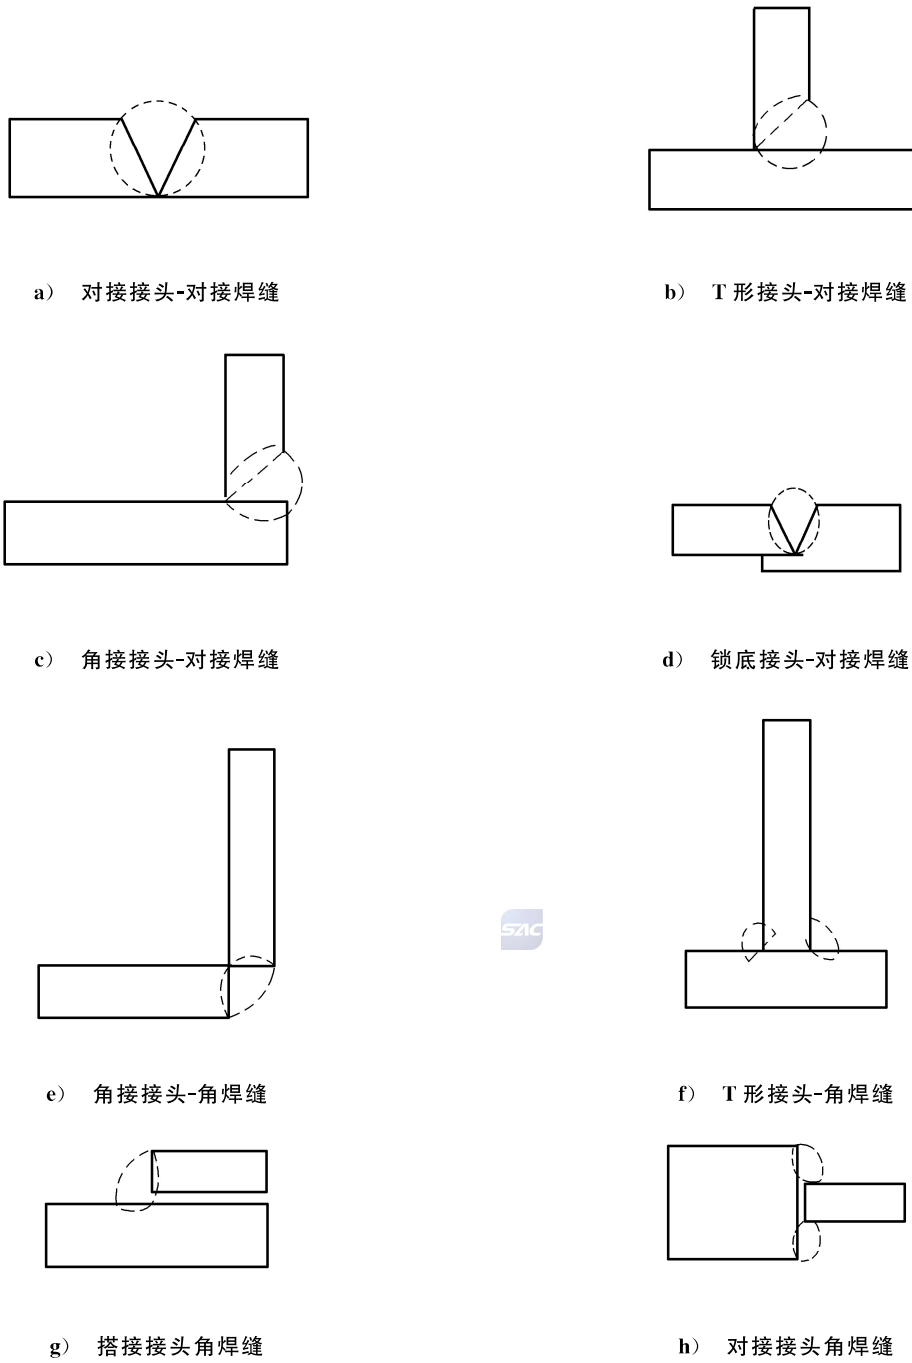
对接焊缝、角焊缝与焊接接头形式
